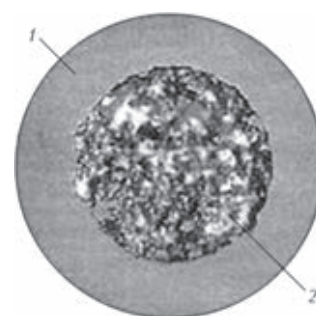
Порошковый присадочный пруток TG-X в разрезе: 1 — оболочка из нержавеющей стали; 2 — флюс
